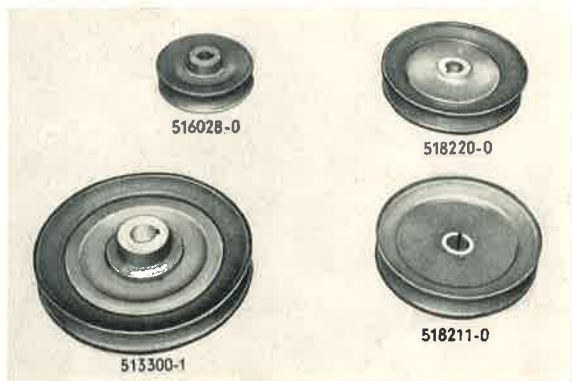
Das sind die vier Riemenscheiben, die bei Erneuerung verwendet werden müssen. Rechts unten die Stahlblech-Scheibe für die 90-W-Lichtmaschine.
